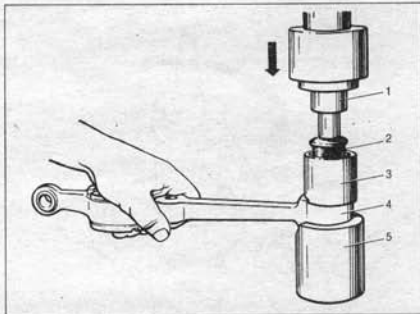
Запрессовка резинометаллического шарнира рычага подвески:
